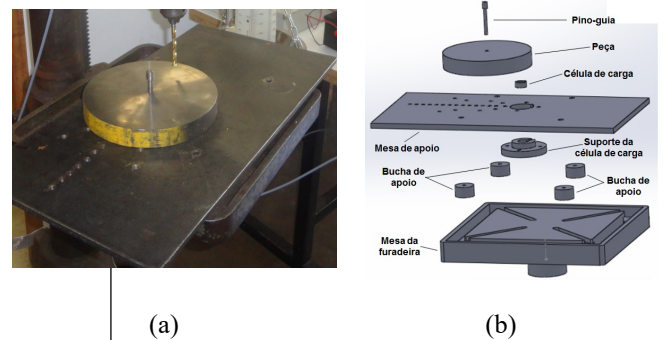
Conjunto sensor de carga/furadeira (a) Montagem; (b) Vista explodida
